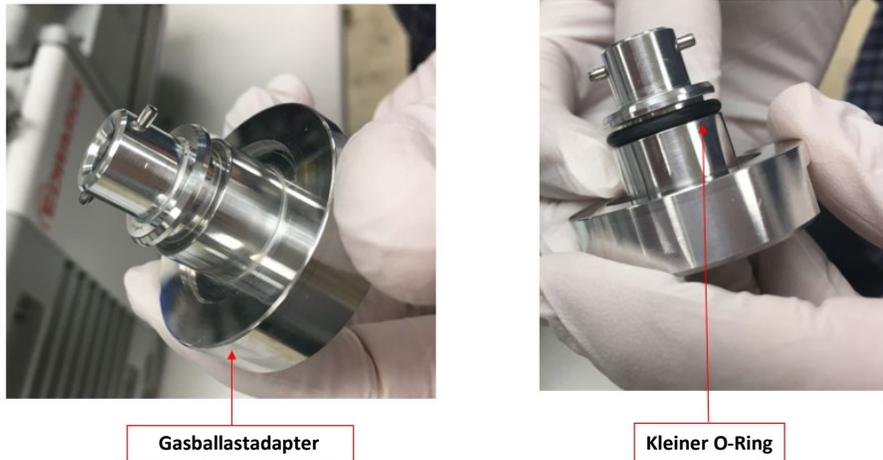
Anbringen des kleinen O-Rings am Gasballastadapter
